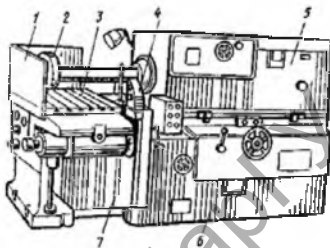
Общий вид планетарного внутришлифовального станка мод. MB6020
